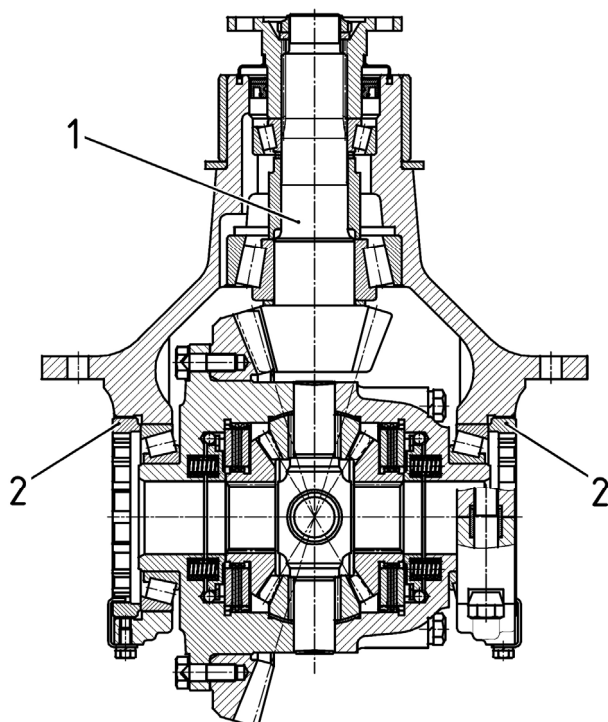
Ведущая шестерня в корпусе центрального редуктора
